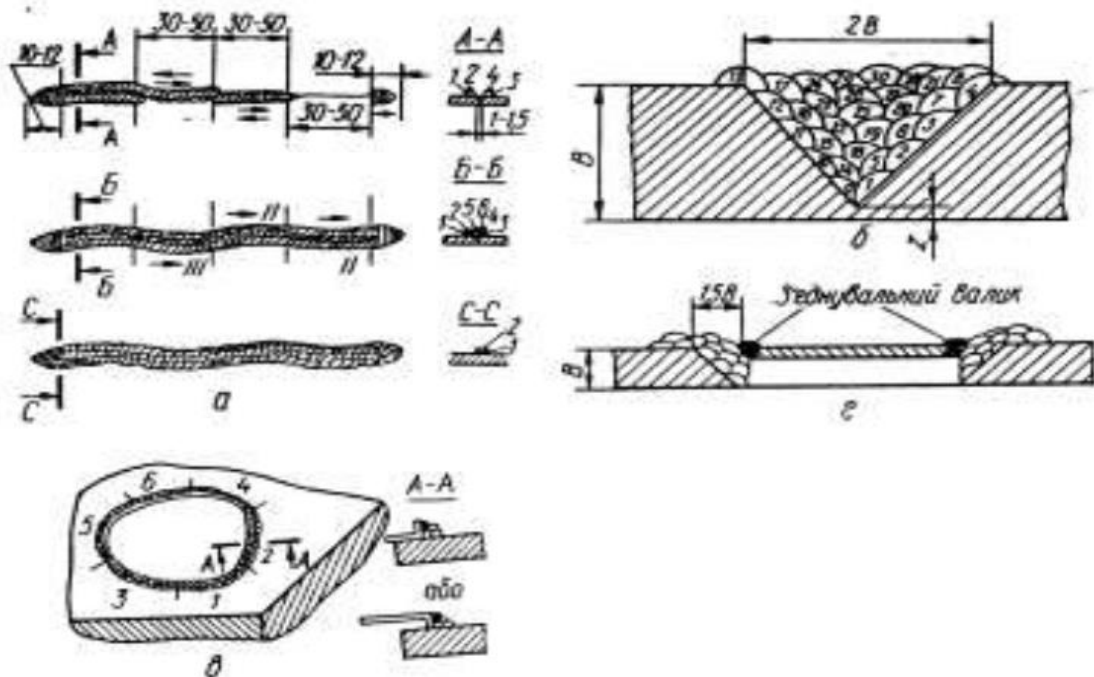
Схема накладання швів при зварюванні чавунних корпусних деталей: а – тріщин у тонкостінних деталях без наступної механічної обробки; б – тріщин у товстостінних деталях з наступною механічною обробкою; в – підготовка пробоїн і порядок зварювання при накладанні латки внапуск; г – зварювання вставки у пробоїну деталі
